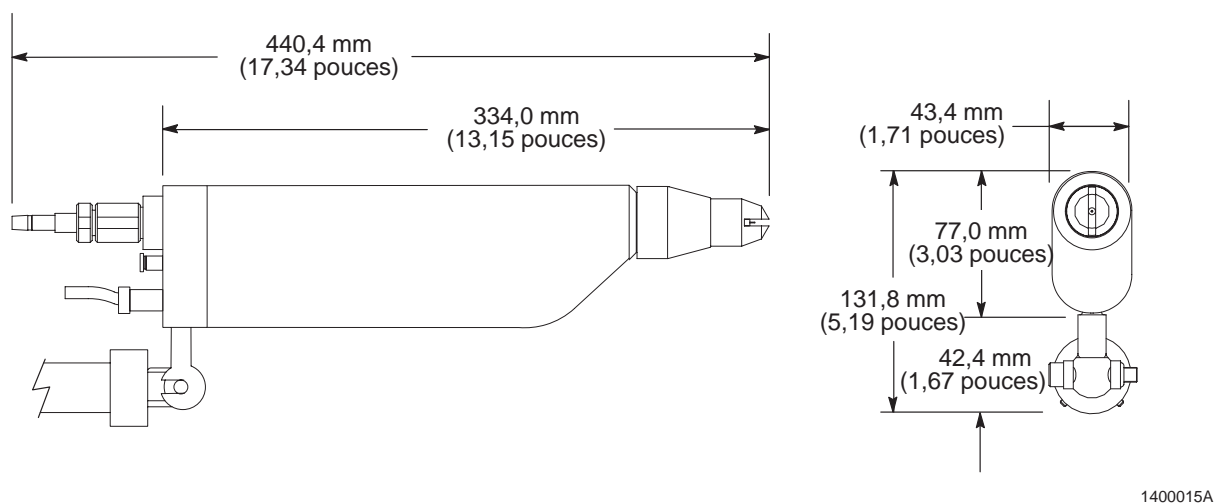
Dimensions du pistolet de poudrage automatique Sure Coat à fixation par barre
